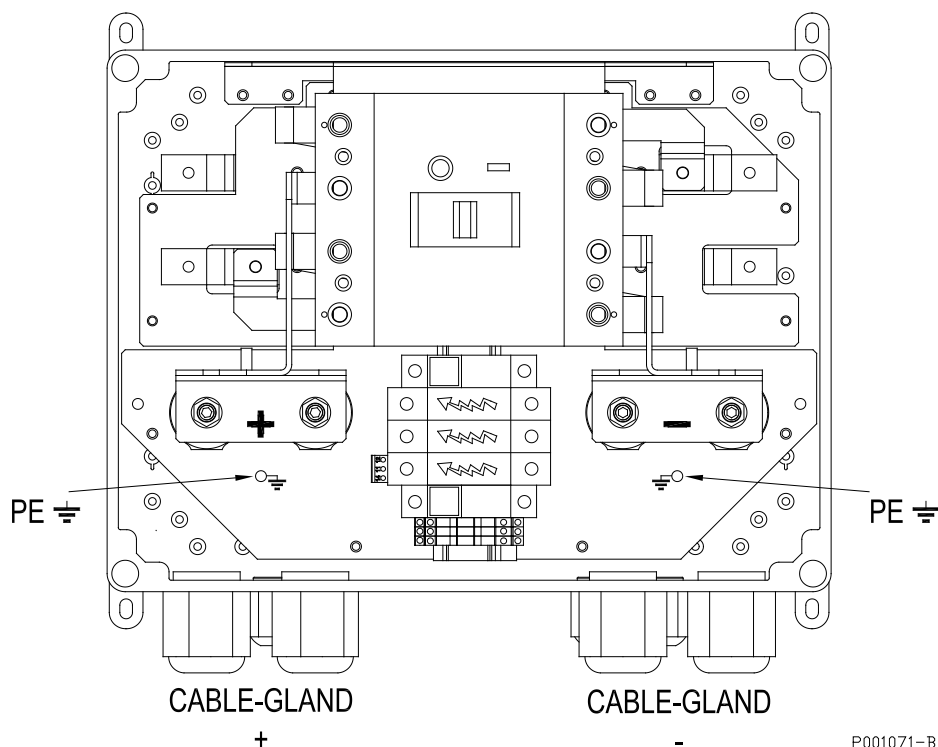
Position der DC SWITCH BOX Kabelverschraubungen
